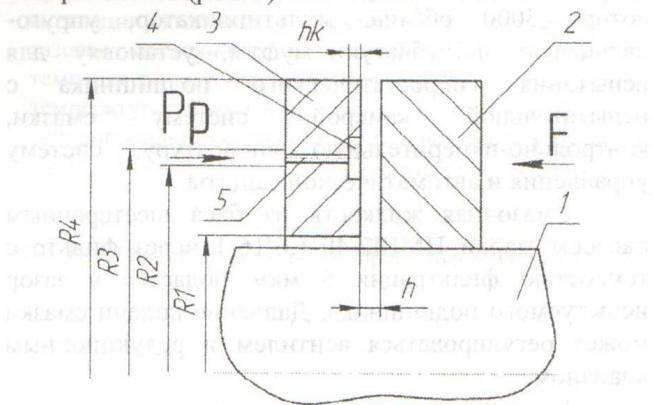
Схема подшипника: 1 - ротор; 2 - упорный диск; 3 - рабочая поверхность подшипника; 4 - камера нагнетания; 5 - дроссель
